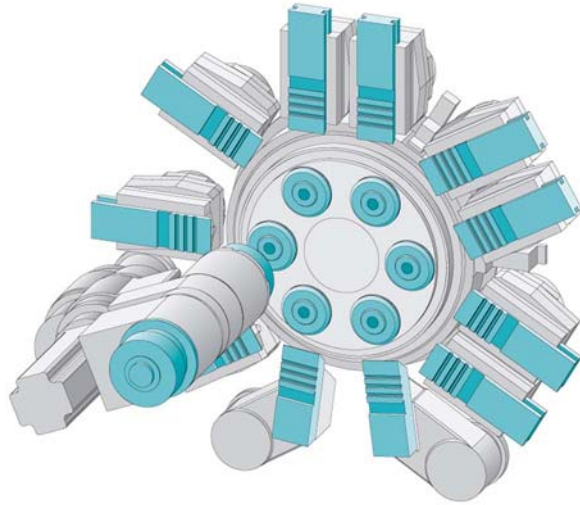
Anordnung der Werkzeugträger bei dem Mehrspindeldrehautomaten mit sechs Spindeln und elf Werkzeugträgern (Werkbild Index)
